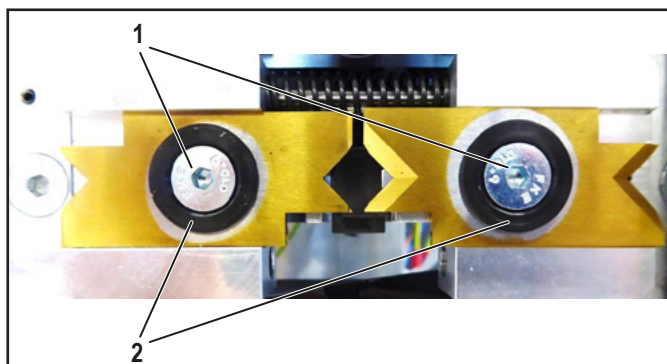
Lames à dénuder pour Power Stripper 6.0, Power Stripper 16
